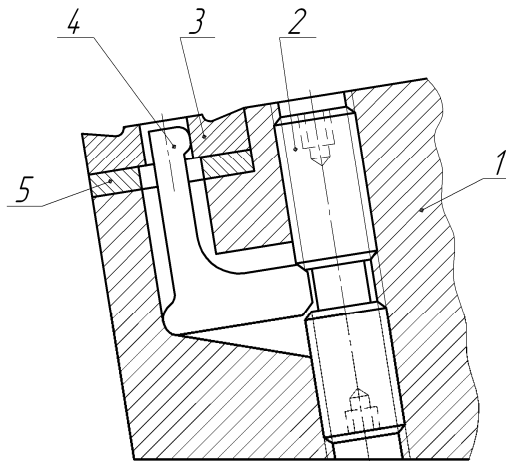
Закріплення пластини через центральний отвір важелем:
